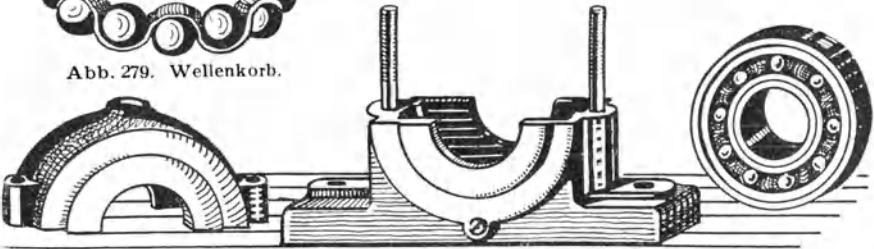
Geteiltes Stehlager mit Spannhülsenlager im Einstellring.
